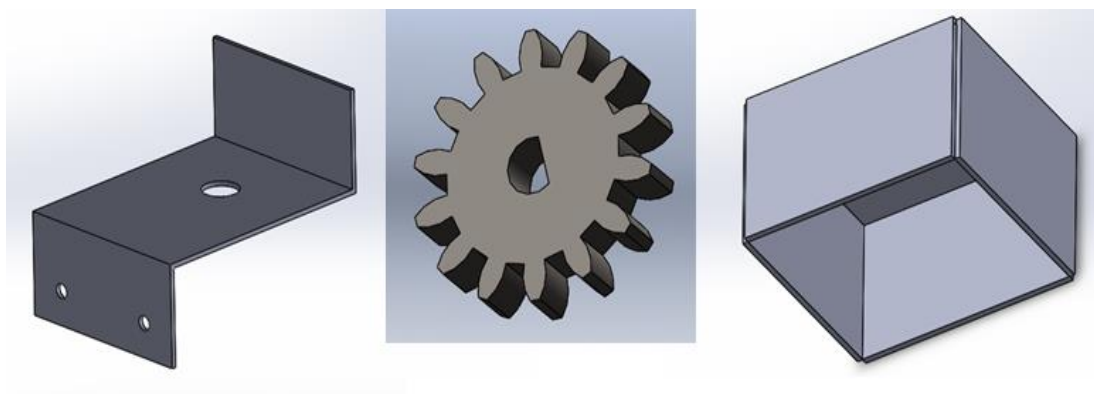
Modelado CAD elementos mecanismo para medición dirección
